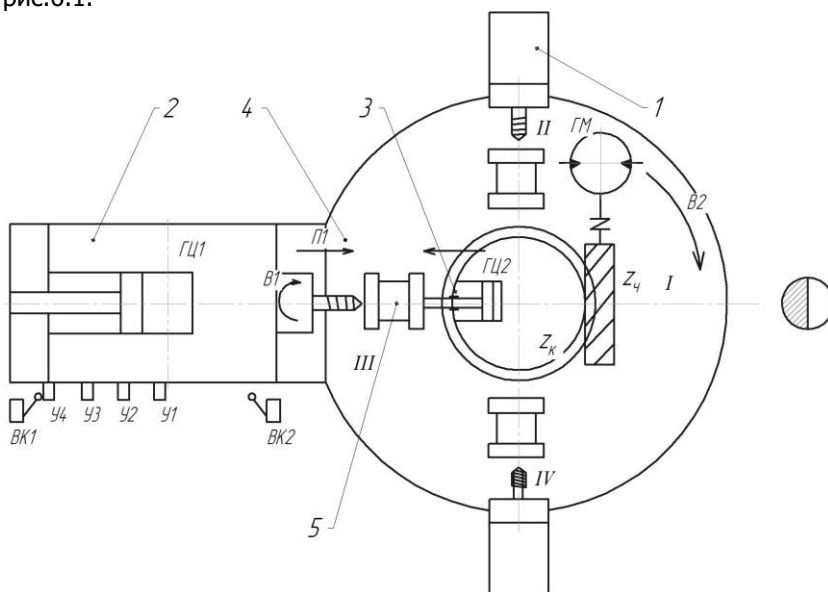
Компоновка агрегатно-сверлильного комплекса
